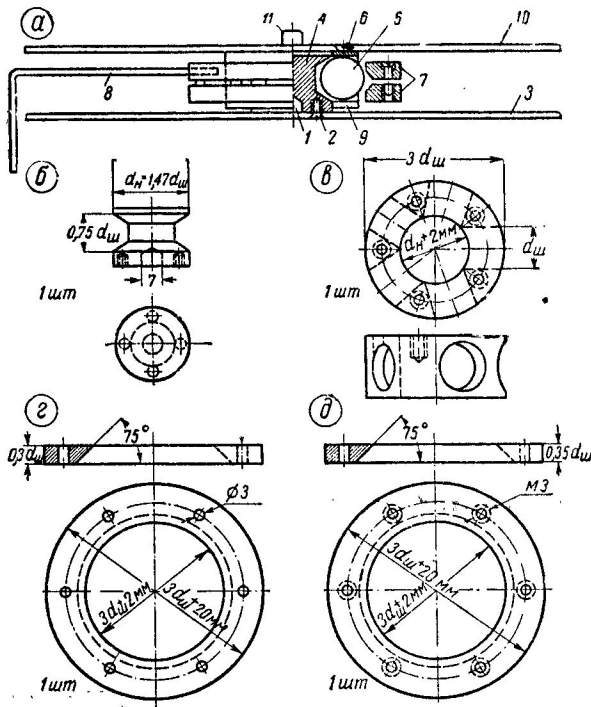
а — разрез приставки в сборе; б — ведущий конус — деталь 4 (материал сталь Ст-4, Ст-5); в — сепаратор — деталь 9 (материал бронза, латунь); г — верхнее кольцо конуса — деталь 7 (материал сталь Ст-20); д — нижнее кольцо конуса (материал сталь Ст-20)
